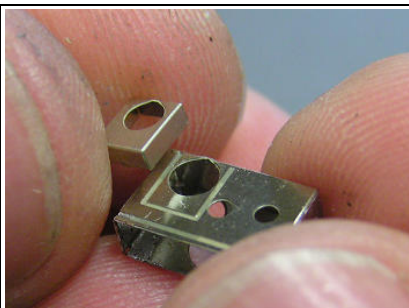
Der gebogene Motorhalter soll genau in die geätzten Nuten des Getriebekastens passen. > Test
